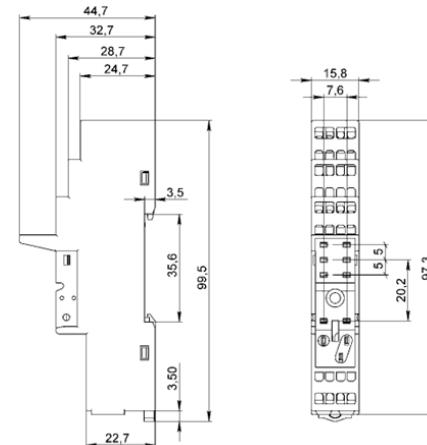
Габаритные, установочные и присоединительные размеры розетки OptiRel G RR95-52
